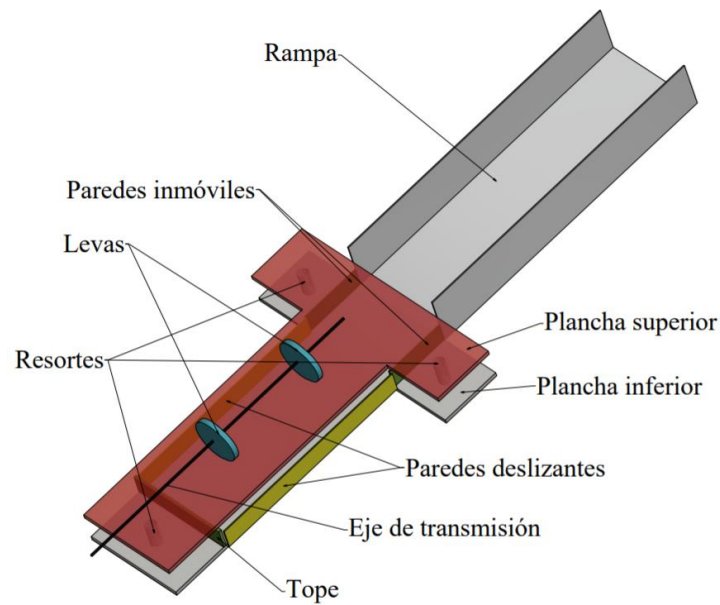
Vista isométrica – Partes del mecanismo de compresión
